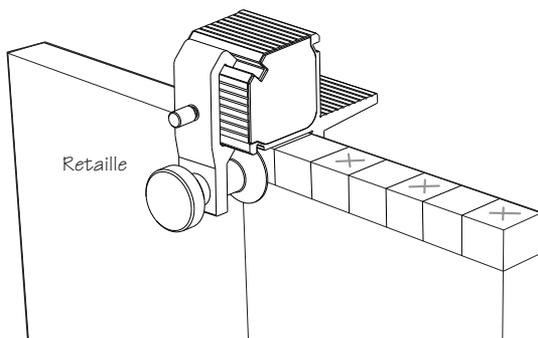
Juxtaposition d'une retaille de bois à la pièce pour stabiliser le guide pendant la coupe de la dernière queue.
